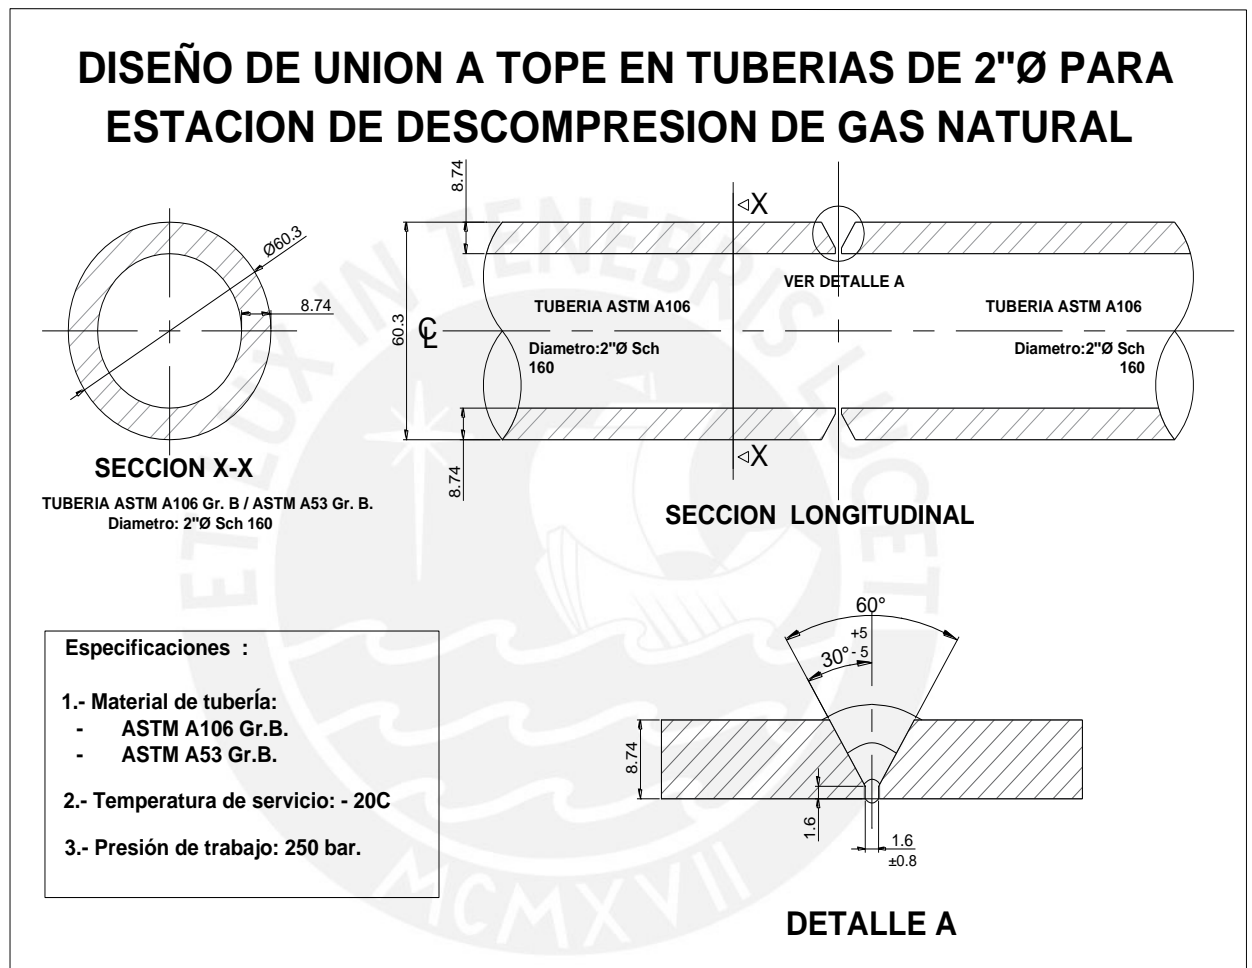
Diseño de junta. Fuente : Elaboración propia
